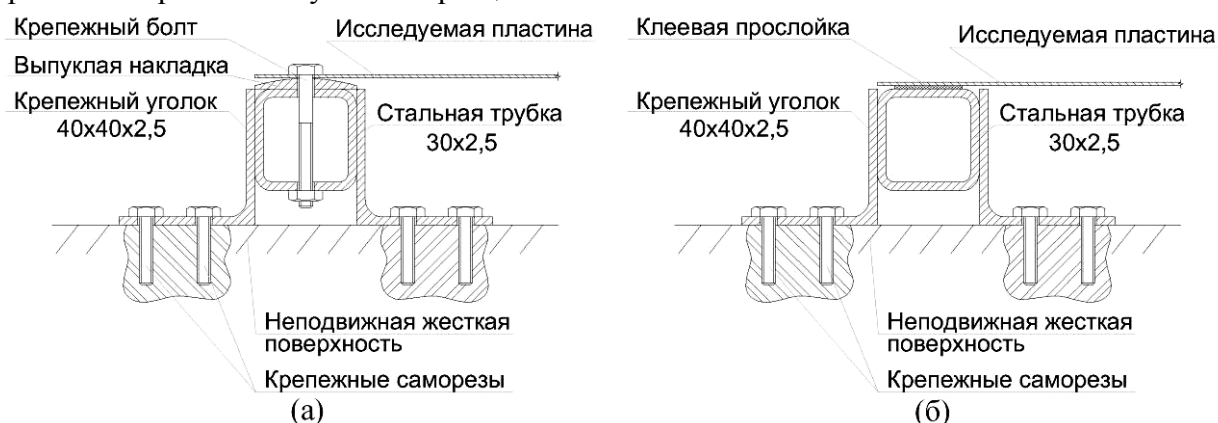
Схемы приспособлений для закрепления краев образцов: а – шарнирного опирания; б – жесткого защемления
